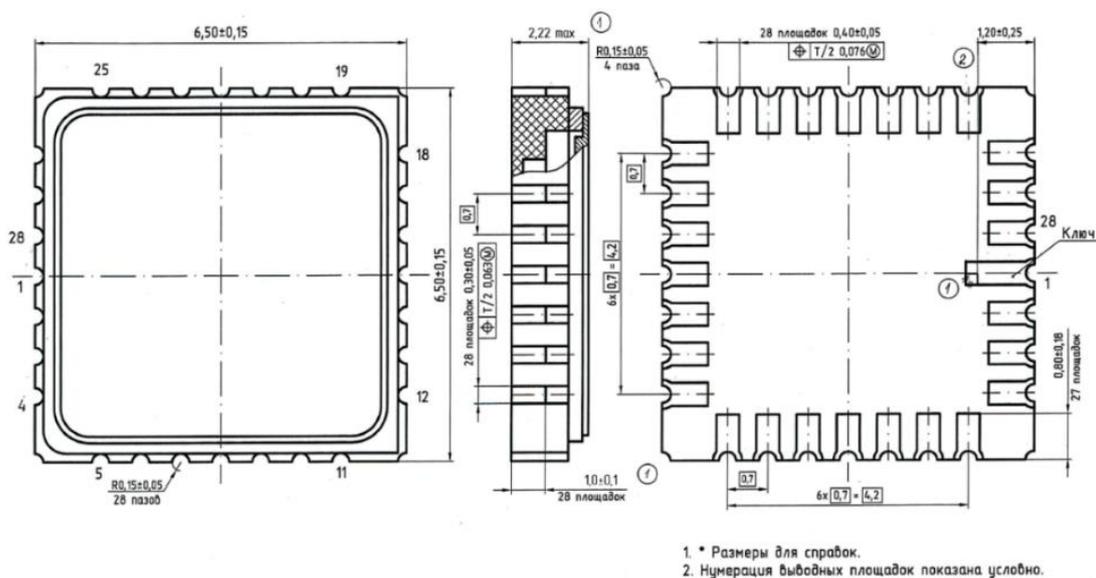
Габаритный чертёж корпуса 5123.28-1.01 (размеры в мм)
